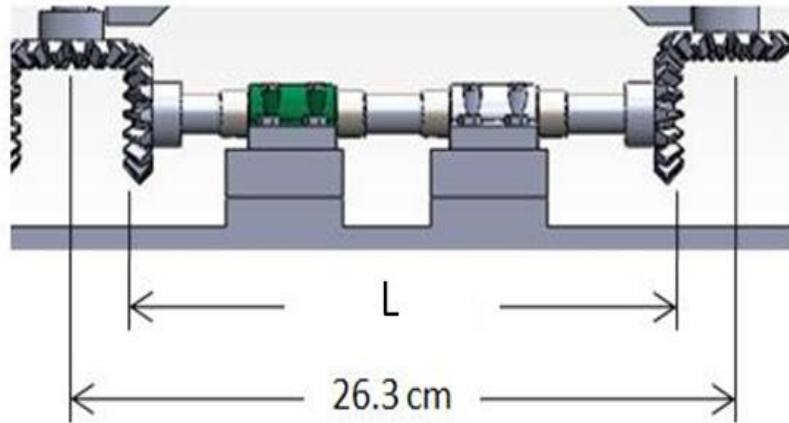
Imagen del ensamble horizontal del mecanismo
